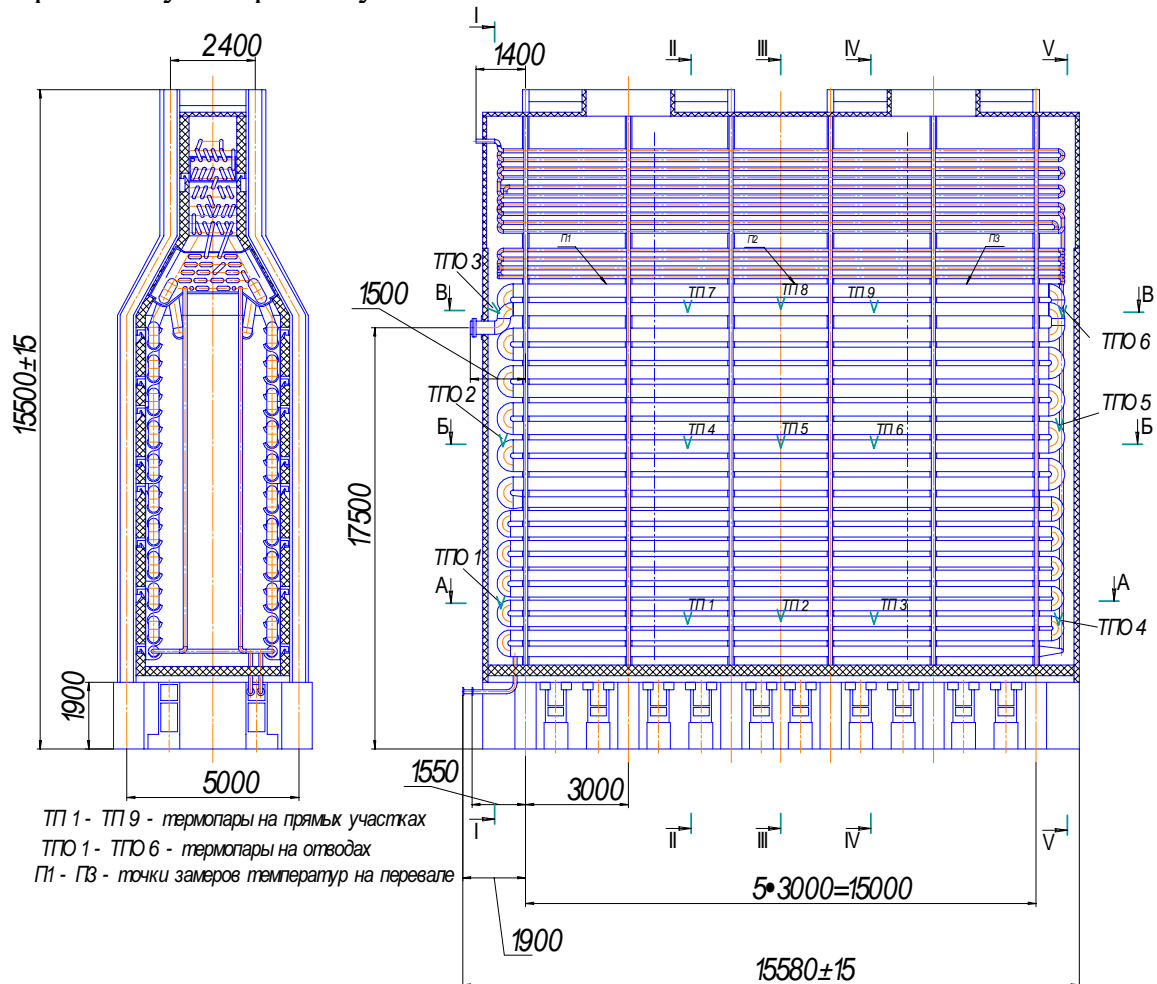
Общий вид нагревательной печи блока подготовки сырья установки АВТМ-9
